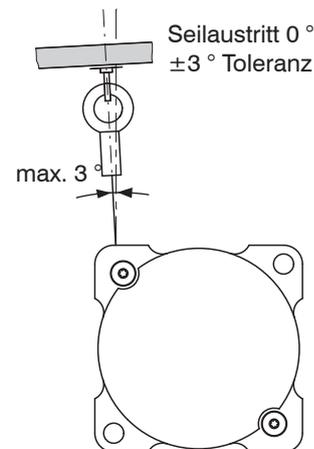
Befestigung und maximaler Schrägzug des Messseils
